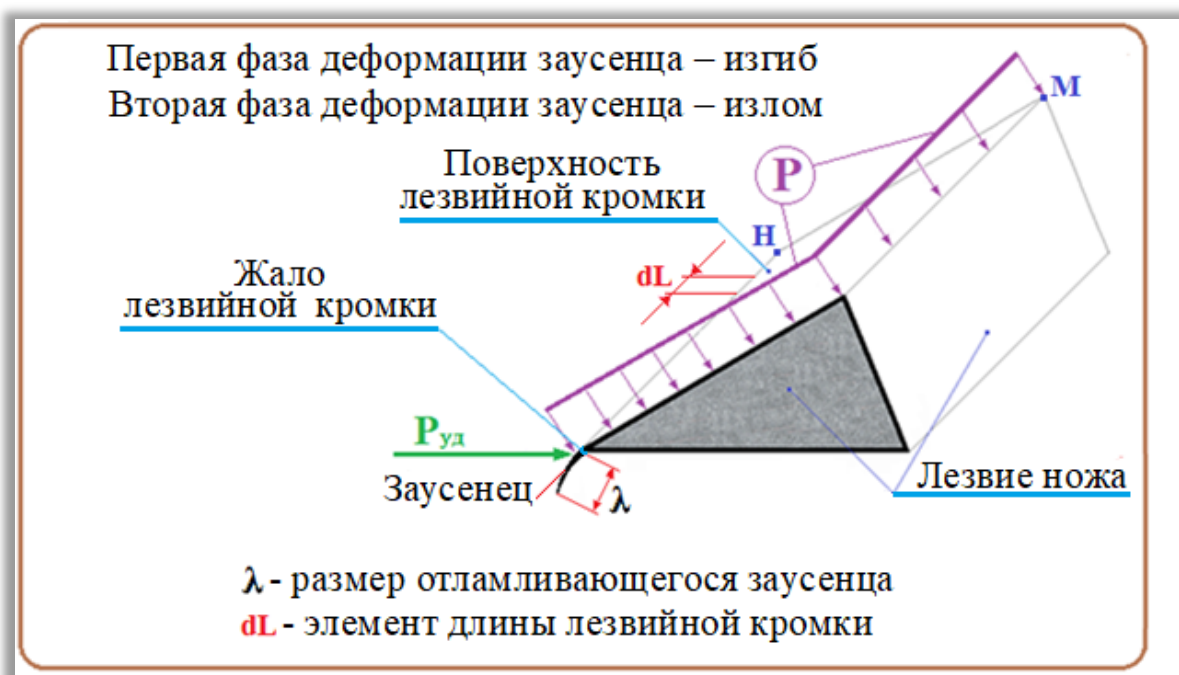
Схема изгиба заусенца и формирования жала лезвийной кромки ножа
